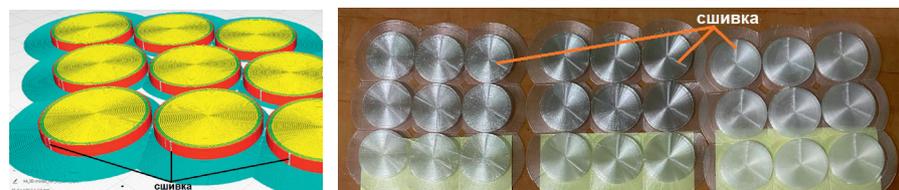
Заготовки из полимерного пластика ПЭТГ (на примере заготовки толщиной 2,0 мм)
